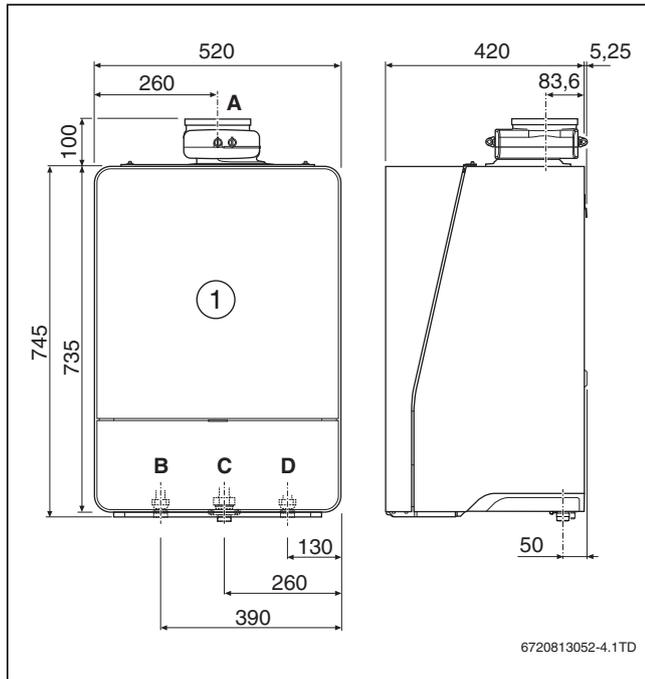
Abmessungen und Anschlüsse¹⁾ GC9000iW ... H
